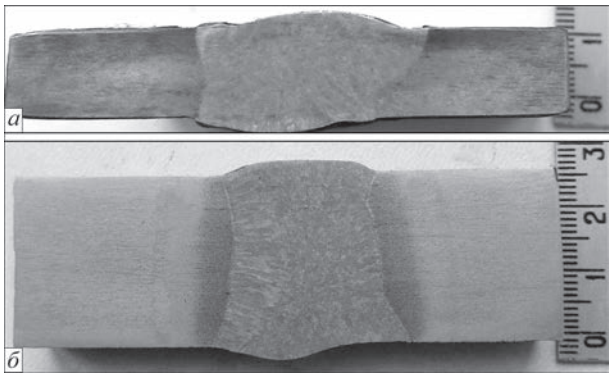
Поперечні макрошліфи зварних з'єднань заготовшки 12 (а) і 25 мм (б)
